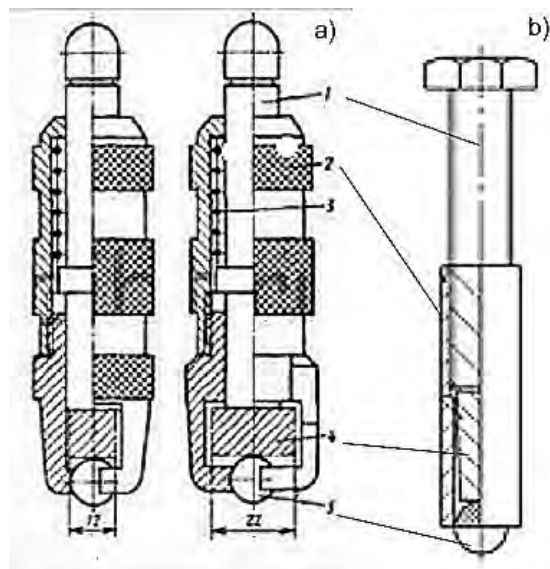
Твердомер «ПОЛЬДИ-ХЮТТЕ» (а) и ударное приспособление (б),
